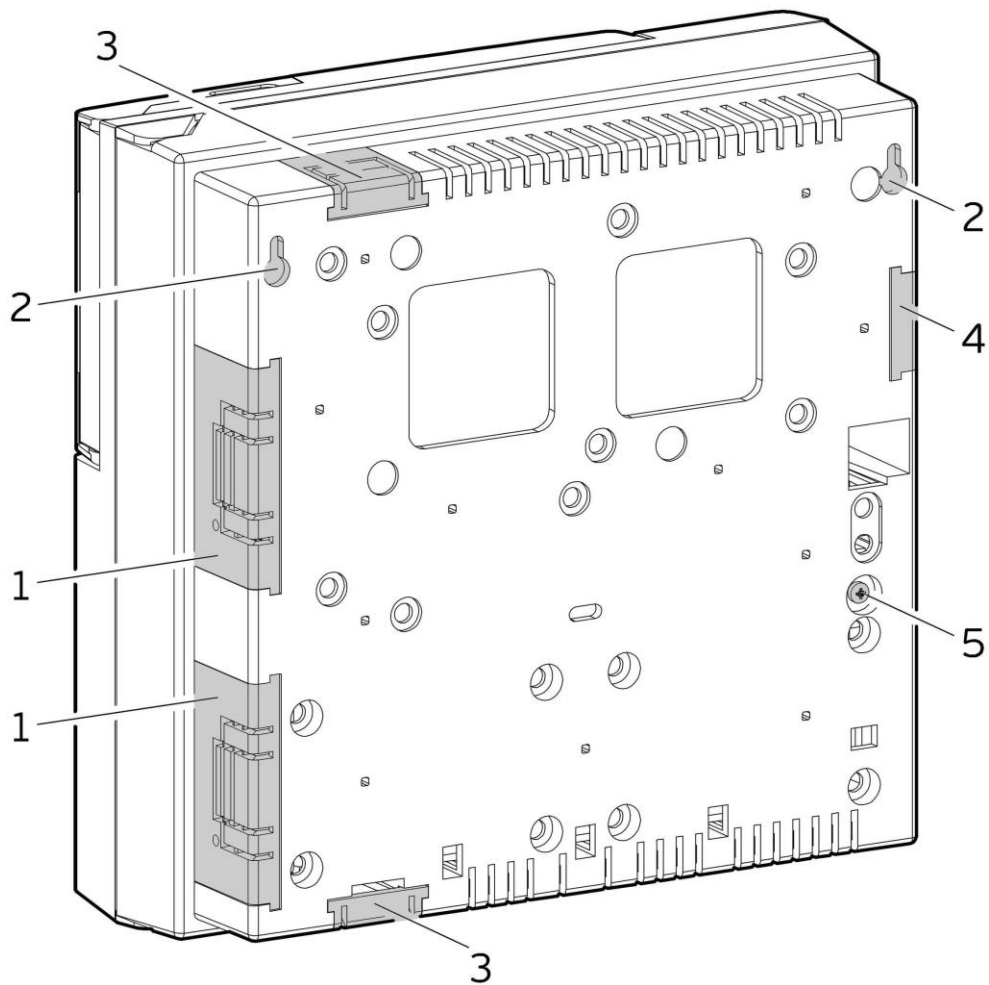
Елементи кріплення і заглушки корпусу ППКО «Дунай-4L»
